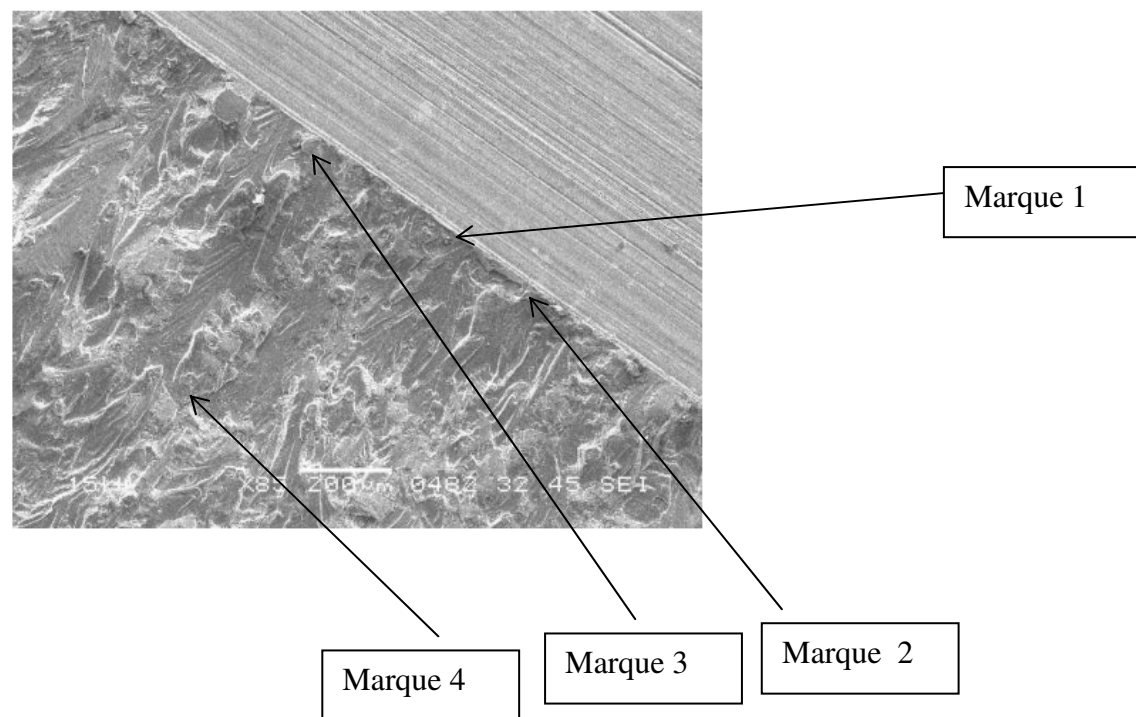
Marques du début d'essai de fissuration
